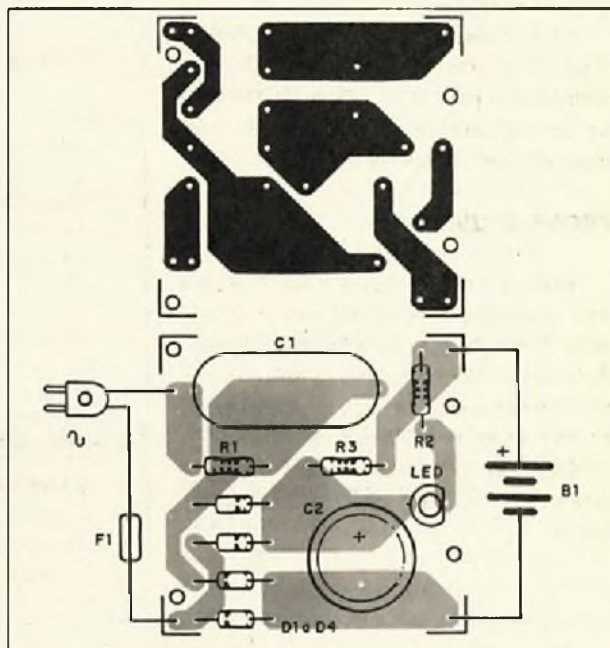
Montagem do carregador na placa (redimensionador a posição de C1 se necessário).
